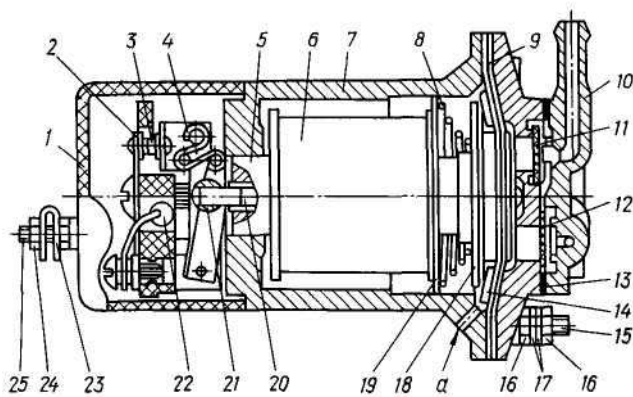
Бензонасос электромагнитный: 1 — крышка; 2 — контакт неподвижный с пластиной в сборе; 3 — контакт подвижный с рычажным устройством в сборе; 4 — коромысло пружинное; 5 — сердечник электромагнита; 6 — катушка электромагнита; 7 — корпус; 8 — пружина; 9 — диафрагма; 10 — крышка с клапанами в сборе; 11 — клапан нагнетательный; 12 — клапан всасывающий; 13 — прокладка крышки; 14 — шайба опорная немагнитная; 15 — шпилька крепления провода «массы»; 16, 24 — гайка; 17 — шайба; 18 — якорь; 19 — шайба немагнитная; 20 — шток; 21 — бонка резьбовая; 22 — резистор; 23 — зажим клеммный; 25 — болт клеммный; а — отверстие сообщения с атмосферой поддиафрагменной полости
